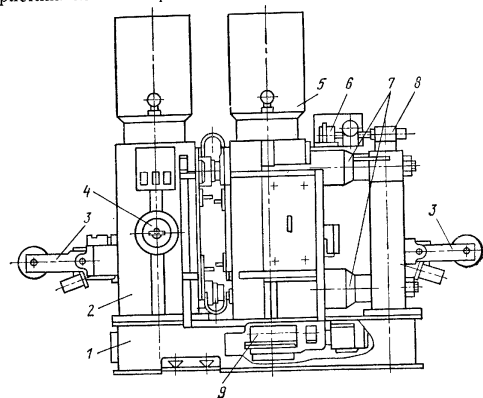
Машина типа К-190П для стыковой сварки оплавлением
